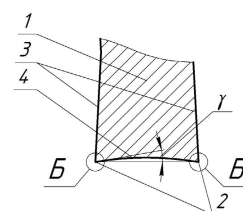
Усовершенствованная конструкция шевера с винтовыми режущими кромками (сечение А-А)
